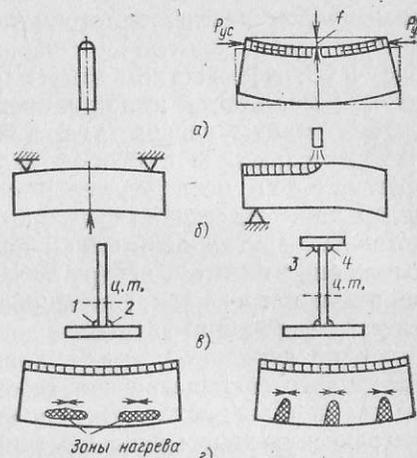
Деформация изгиба сварных заготовок и способы ее устранения
